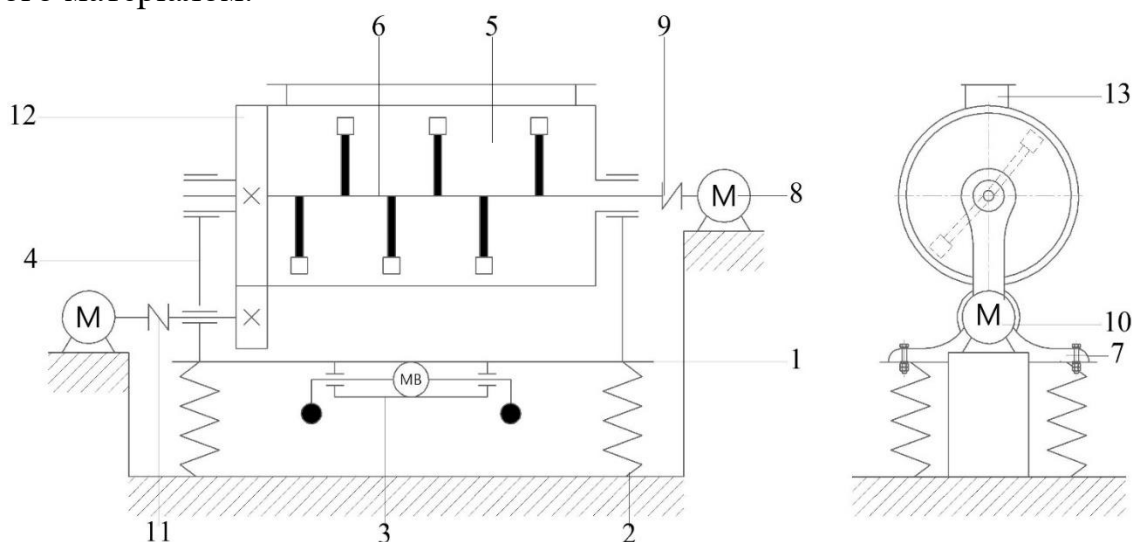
Принципова схема вібровідцентрового змішувача: 1 – корпус; 2 – елементи пружні; 3 – вібробуджувач; 4 – стійка; 5 – контейнер; 6 – вал лопатевий; 7 – опора; 8, 10 – електродвигун; 9, 11 – муфта; 12 – передача зубчаста; 13 – люк
